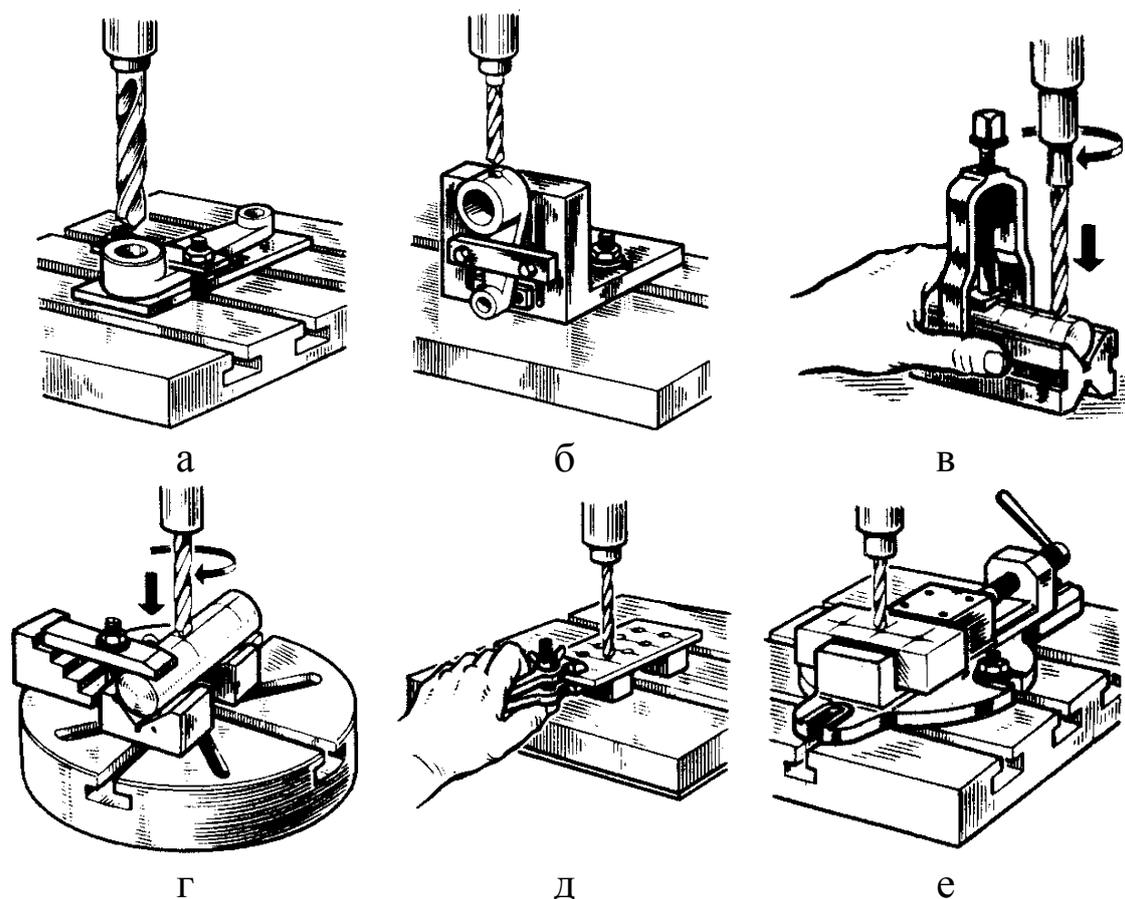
Крепление заготовок при сверлении: а - непосредственно на столе планками; б - на угольнике планками; в - на призме хомутиком; г - на призме планкой со ступенчатой опорой; д - в ручных тисках на подкладках; е - в машинных тисках
